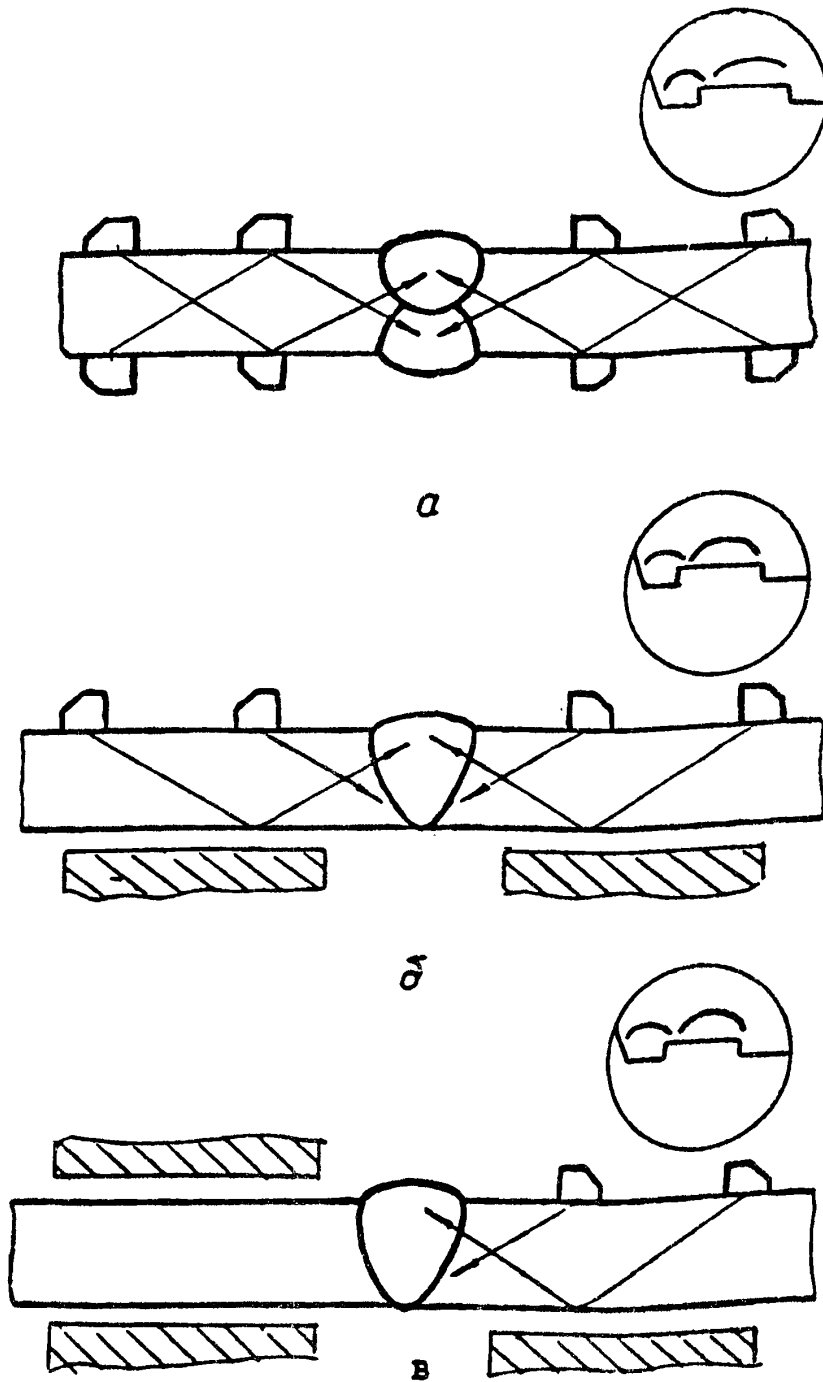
Схемы контроля стыковых сварных соединений без подкладных пластин:
